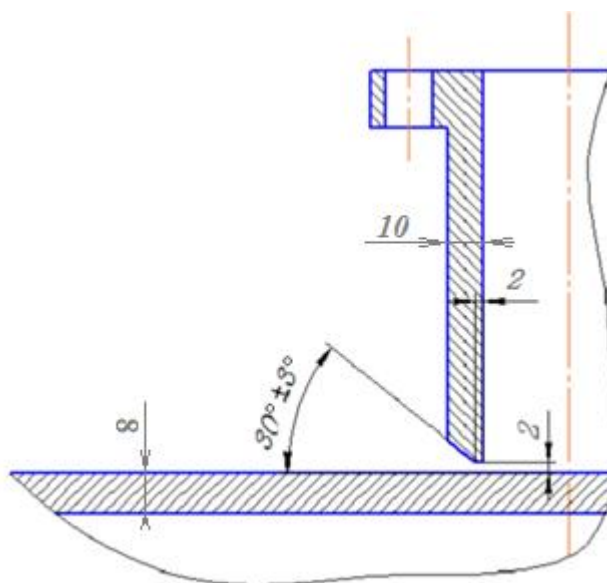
Подготовка кромок для сварки
